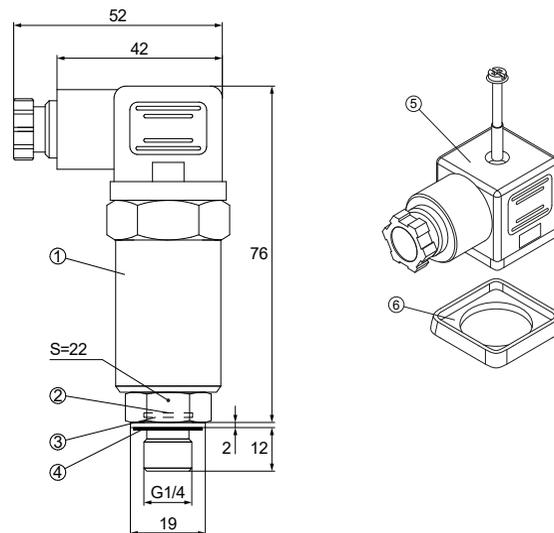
Габаритные размеры датчика и позиционные обозначения элементов конструкции
